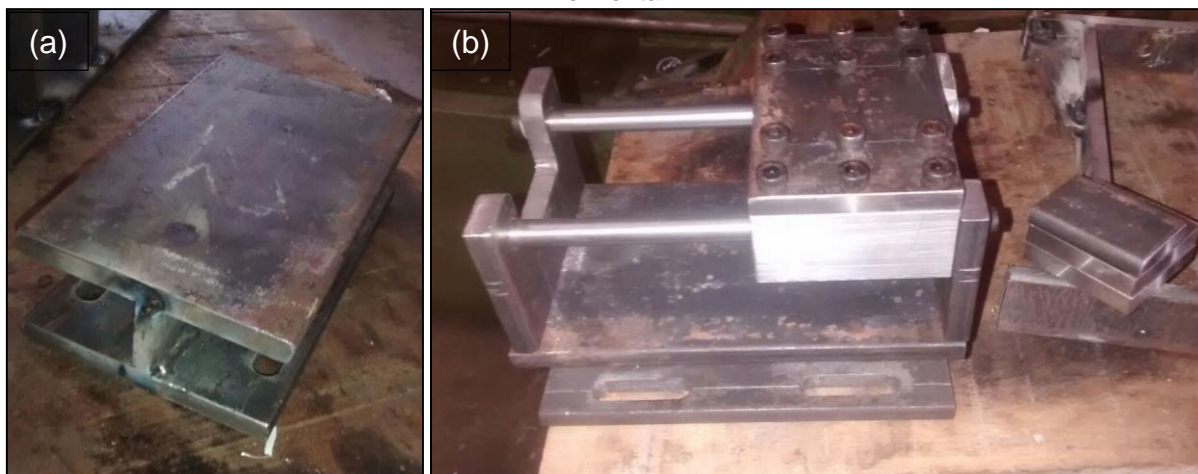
Dispositivo DCB com conjuntos torre DCB e impactador após pinturas.
